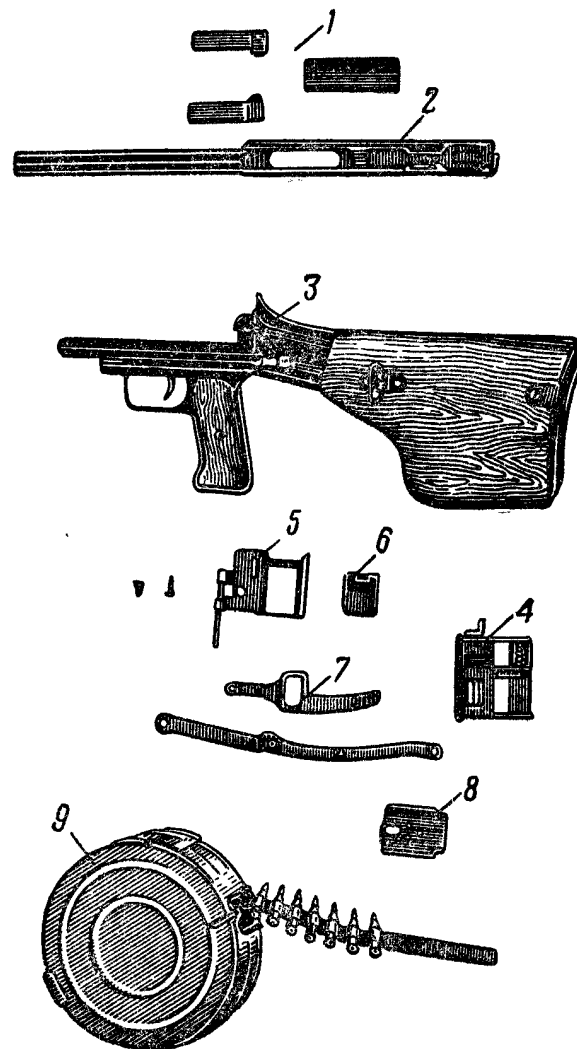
Части и механизмы ручного пулемета Дегтярева (РПД), собираемые на станке:
